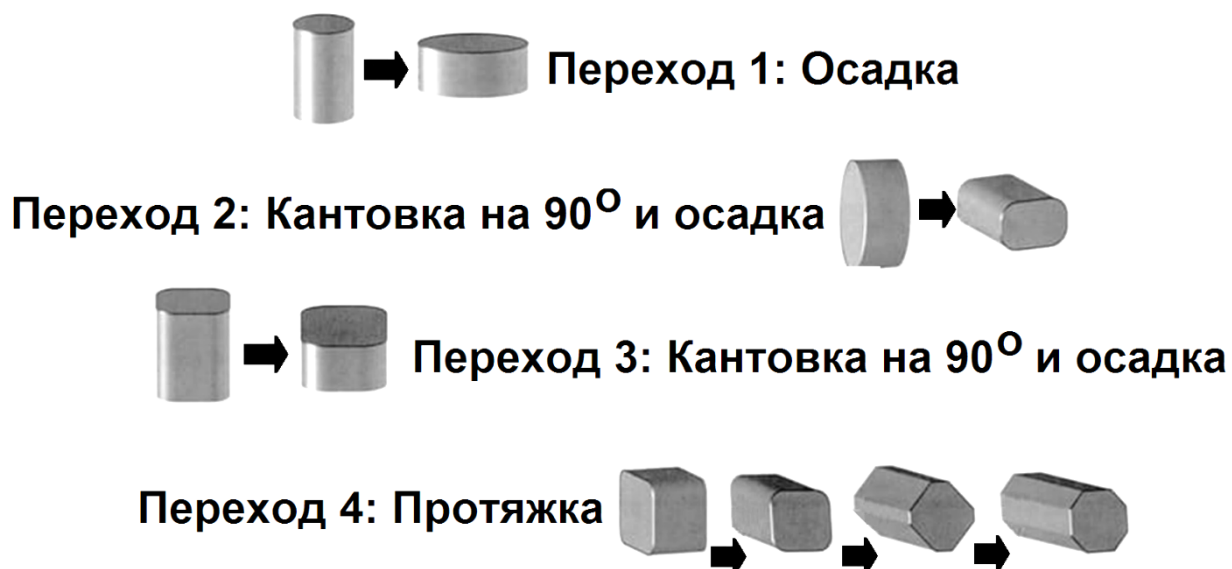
схема всесторонней ковки [5,89,90].
